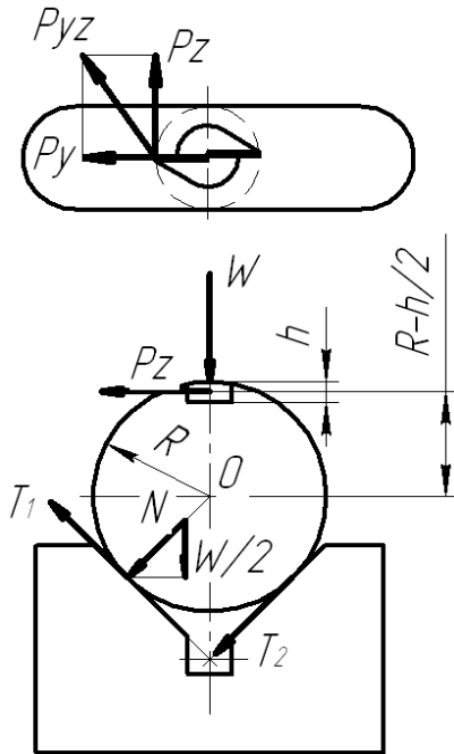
Схема сил при фрезеруванні шпонкового пазу
